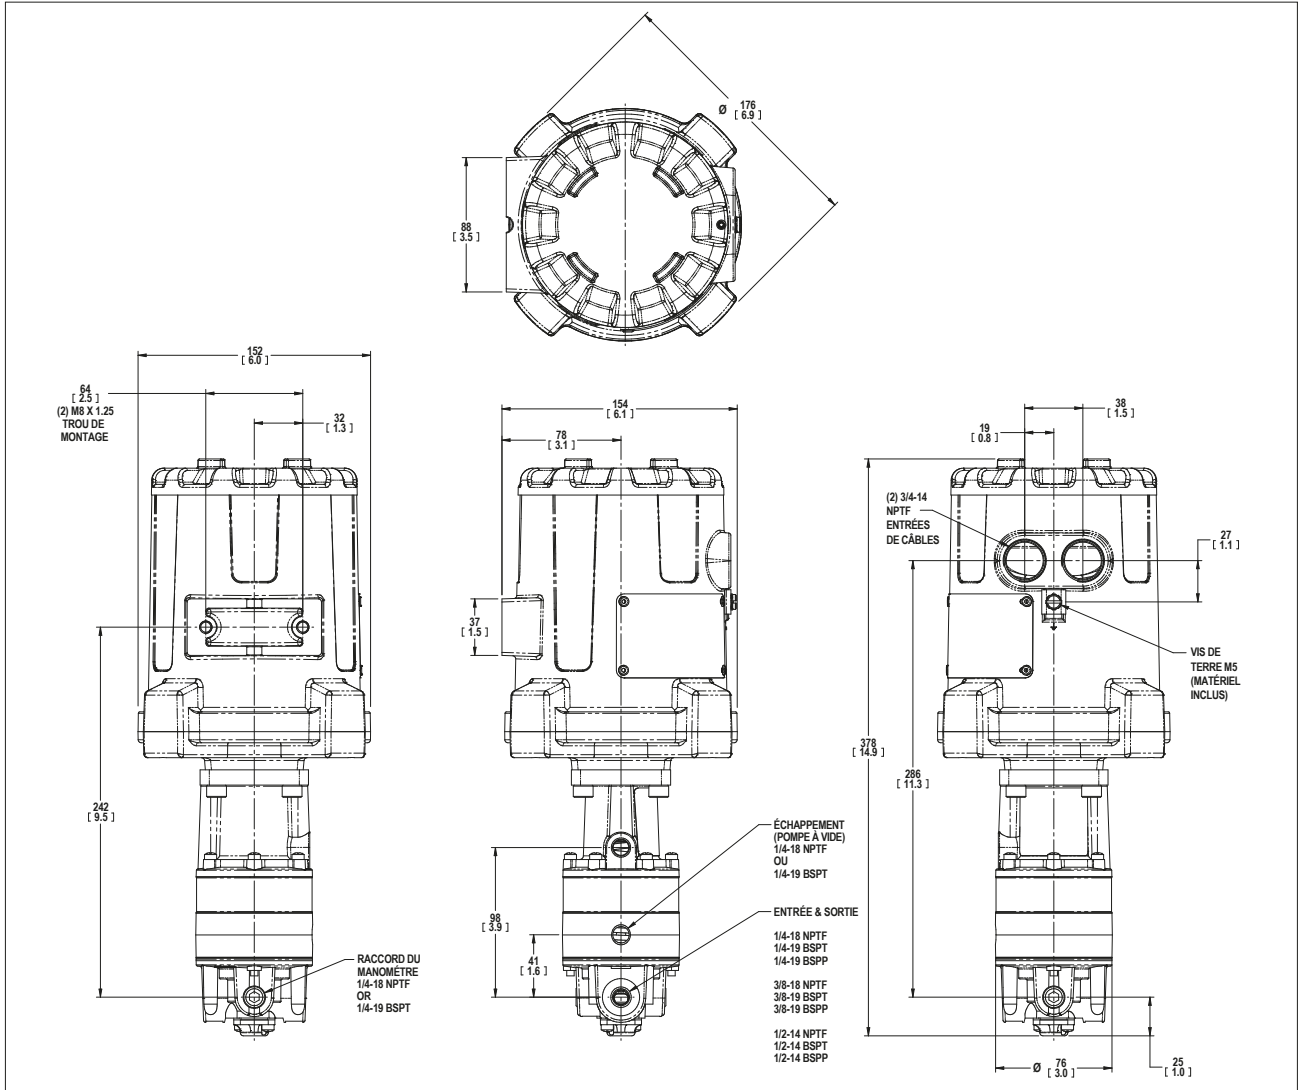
Dimensions d'installation de la motorisation PAX1 et du modèle 16
